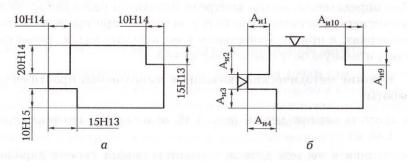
Варианты (а и б) обрабатываемой детали
